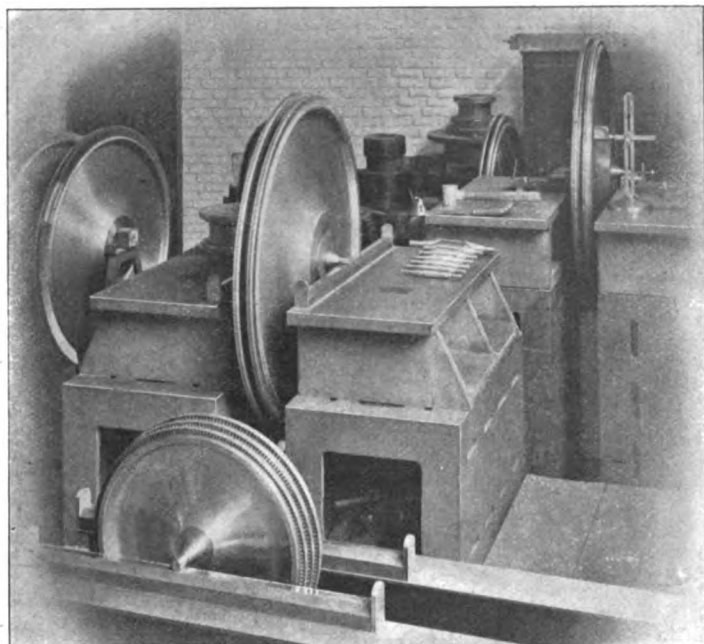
Befestigen der Räder auf den Turbinenwellen.
